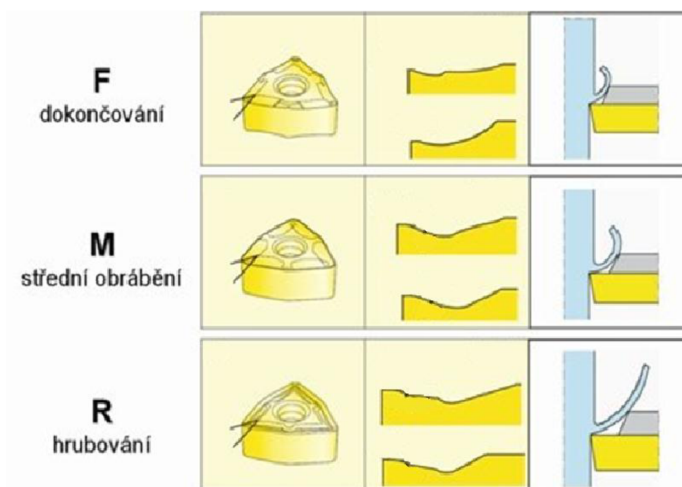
Tříska při obrábění břitovou destičkou 3
